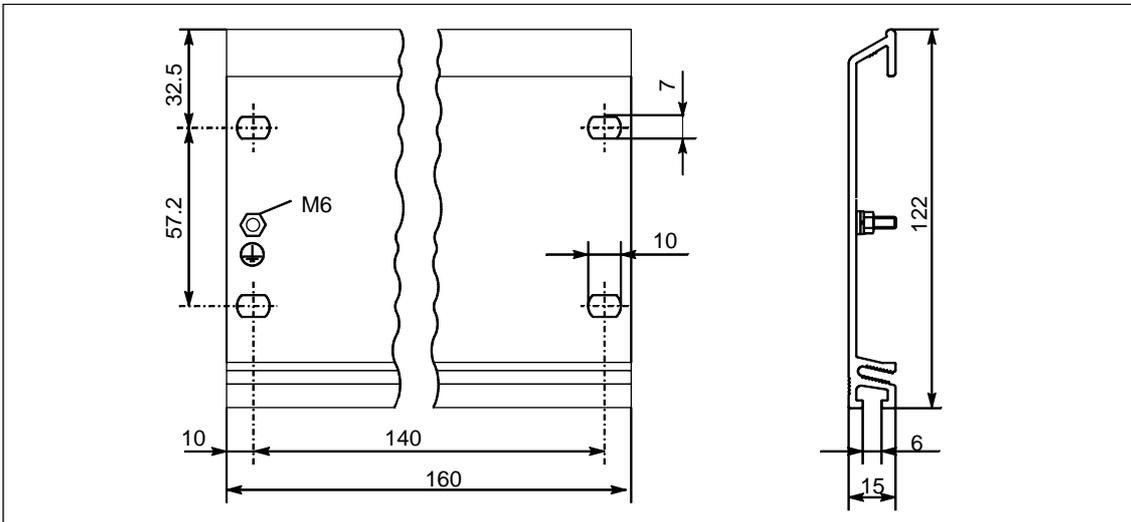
Чертеж с размерами профильной шины стандартной ширины 160 мм
